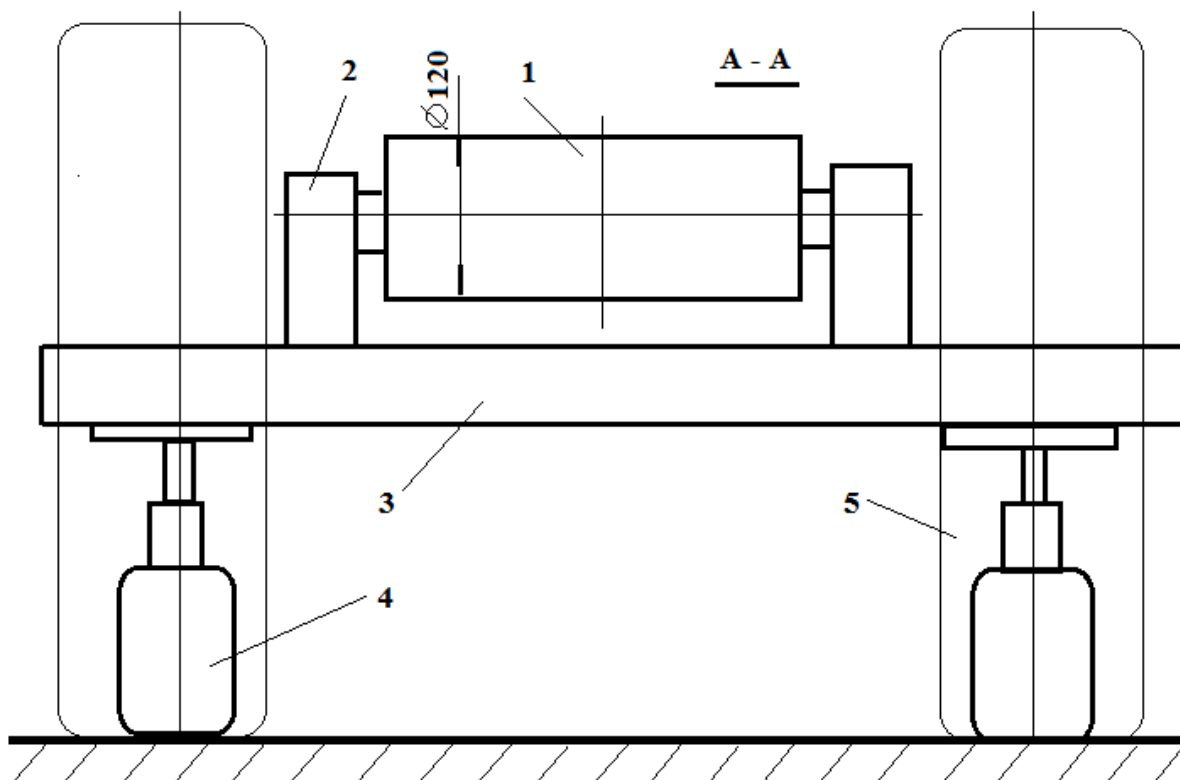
Схема устройства для отгибания переднего конца листа: 1- неприводной ролик, 2- корпус крепления ролика, 3-плита, 4-гидроцилиндр, 5- рама
